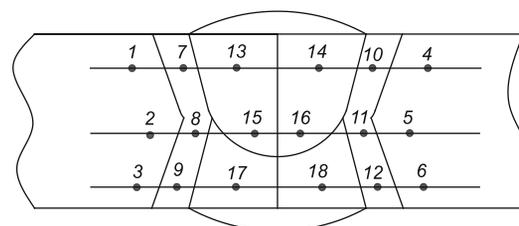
Схема измерения твердости металла сварного соединения:
